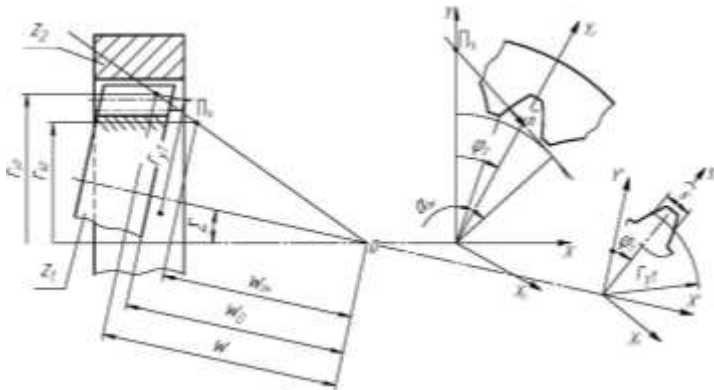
Схема цилиндро-конической передачи внутреннего зацепления
